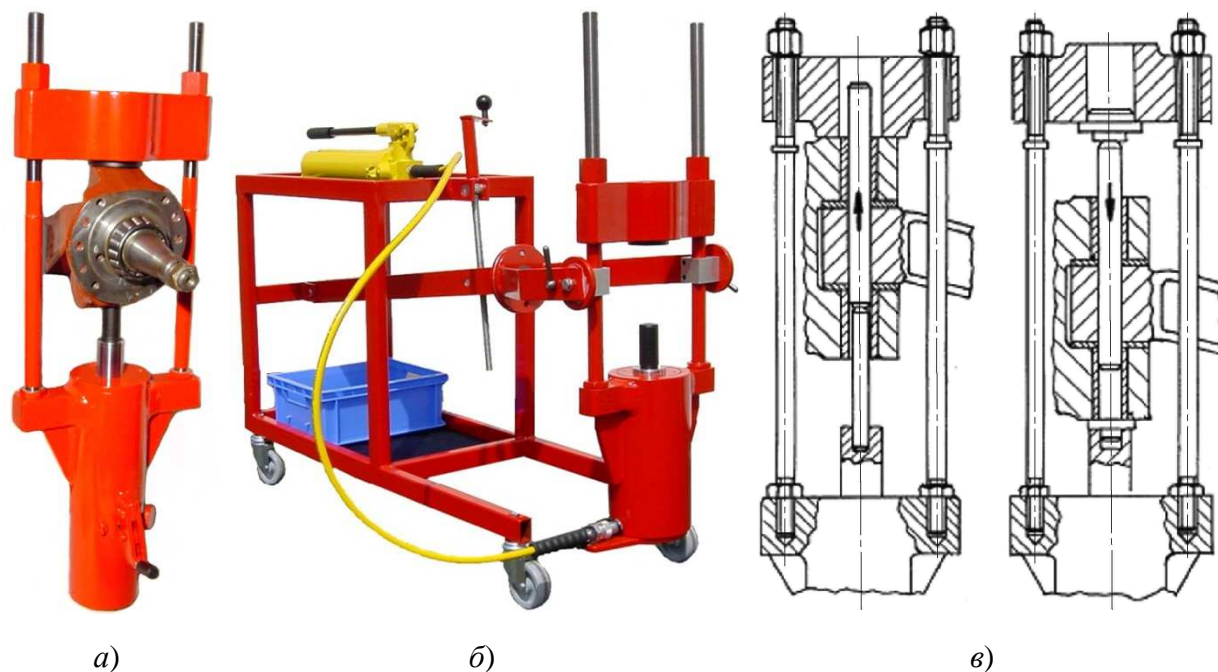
Схема мобильного гидравлического пресса для выпрессовывания и запрессовывания шкворней: *а* – внешний вид пресса; *б* – мобильный пресс в сборе; *в* – схема работы пресса
